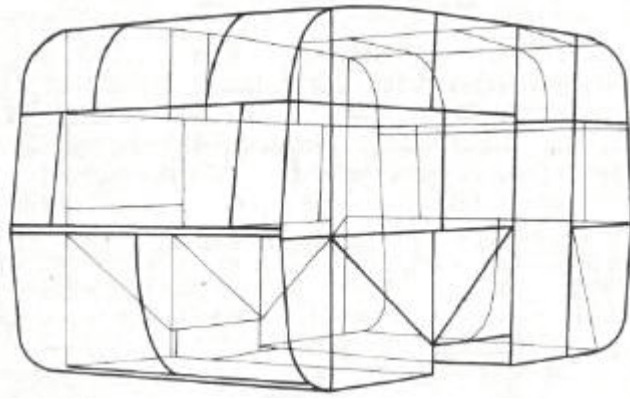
Aus Hohlprofilen zusammengeschweißter Rahmen des Campinganhängers Eriba [11]
